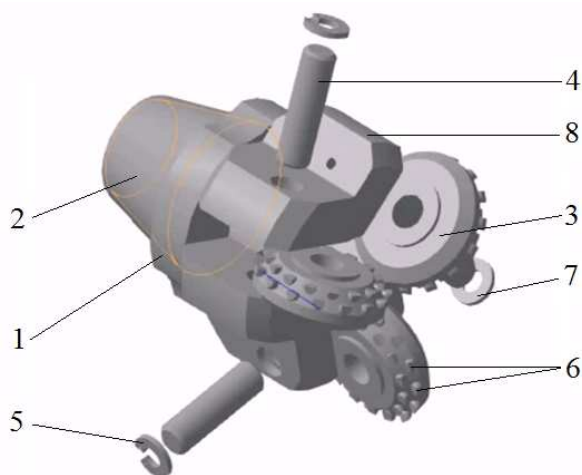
Буровое разборное долото с дисковыми фрезами и двумя рядами твердосплавного вооружения (ДРДФ-244,5-2): 1- корпус, 2 - ниппель, 3 - дисковые фрезы, 4 - ось, 5 - стопорное кольцо, 6 - двухрядное вооружение, 7 -шайбы, 8 - лапы.
